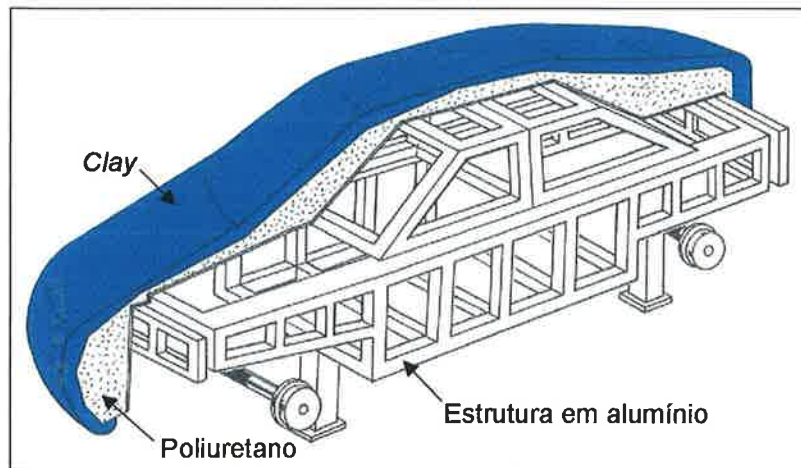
Esquema em corte do modelo construído sobre a base e a estrutura. (adaptado de Yamada, 1993).
